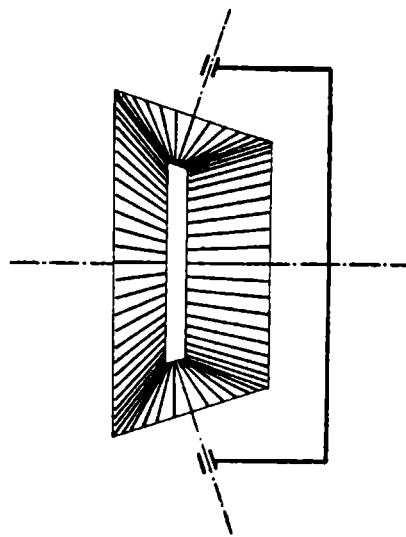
Mecanismo reductor de velocidad por engranajes cónicos y ejes oblicuos.
